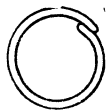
Заготовка труб, свариваемой внакладку.
